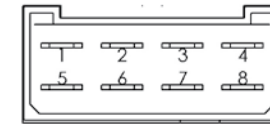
CONNETTORE FASTON VISTA LATO CONTATTI
